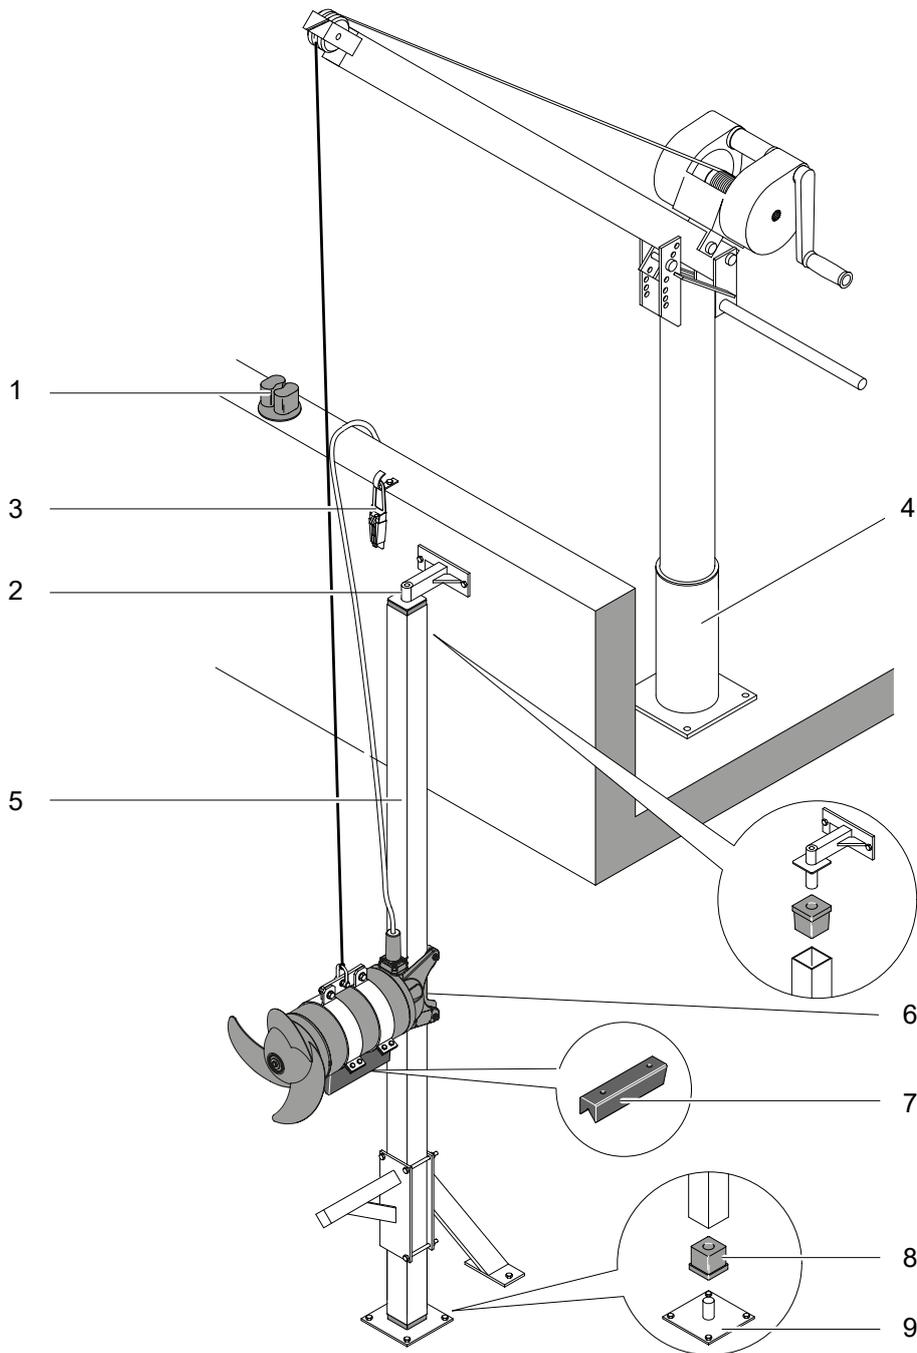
Esempio d'installazione con installazione fissa come acceleratore di flusso
